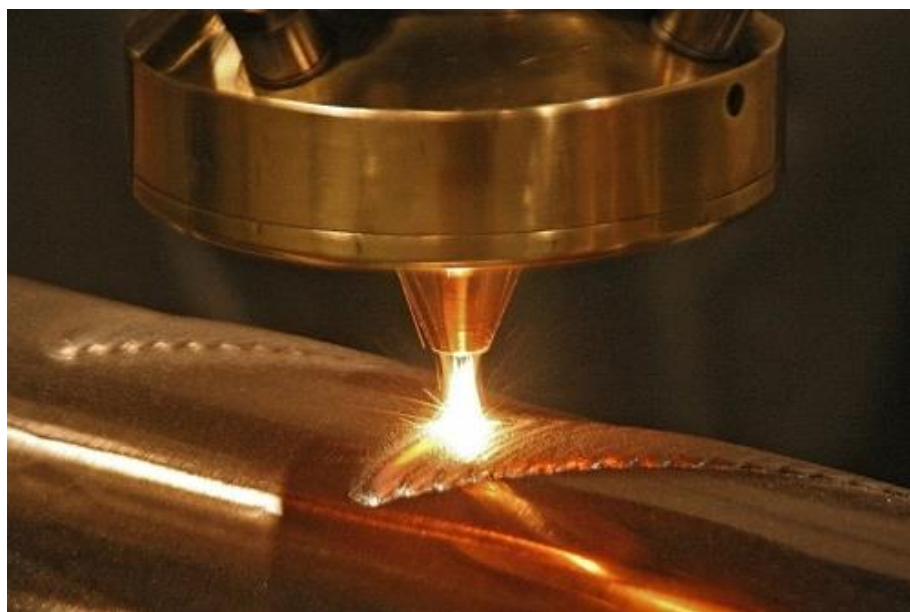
Выкопировка из [12]. Процесс лазерной наплавки
